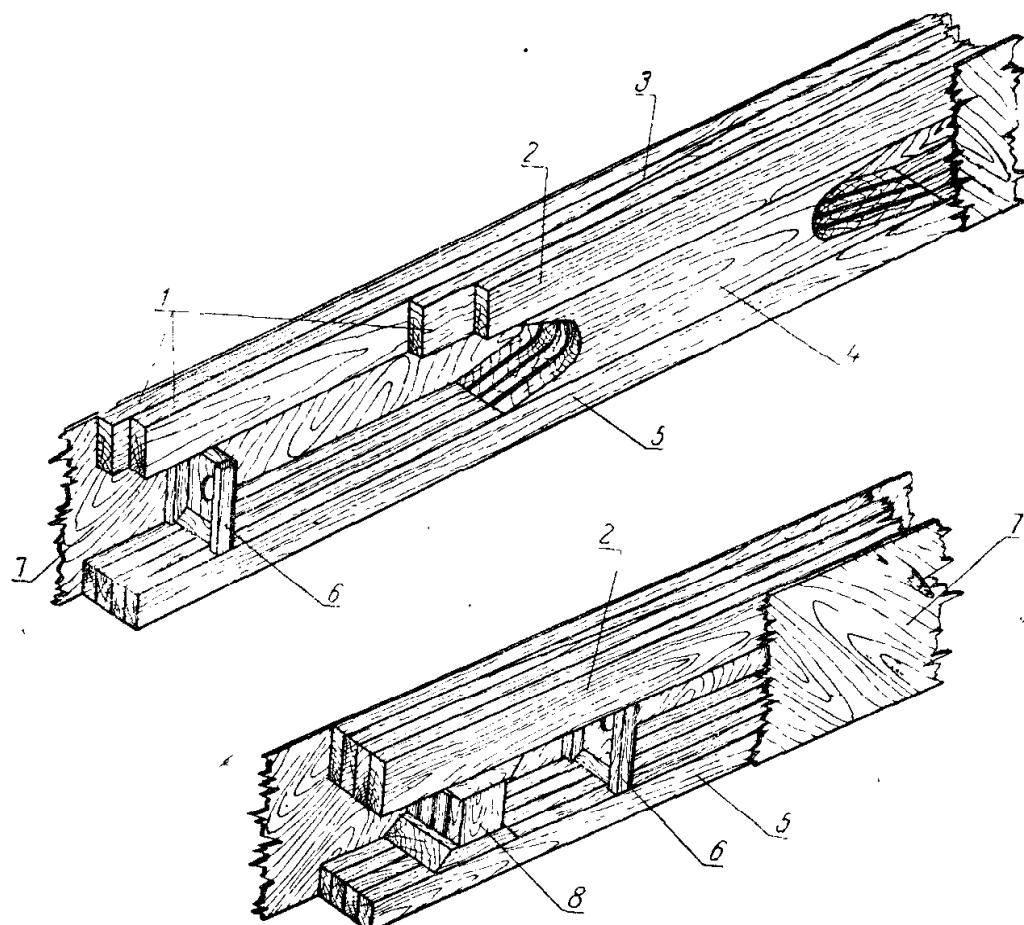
Каркас крыла с установленными узлами и фанерной обшивкой.
